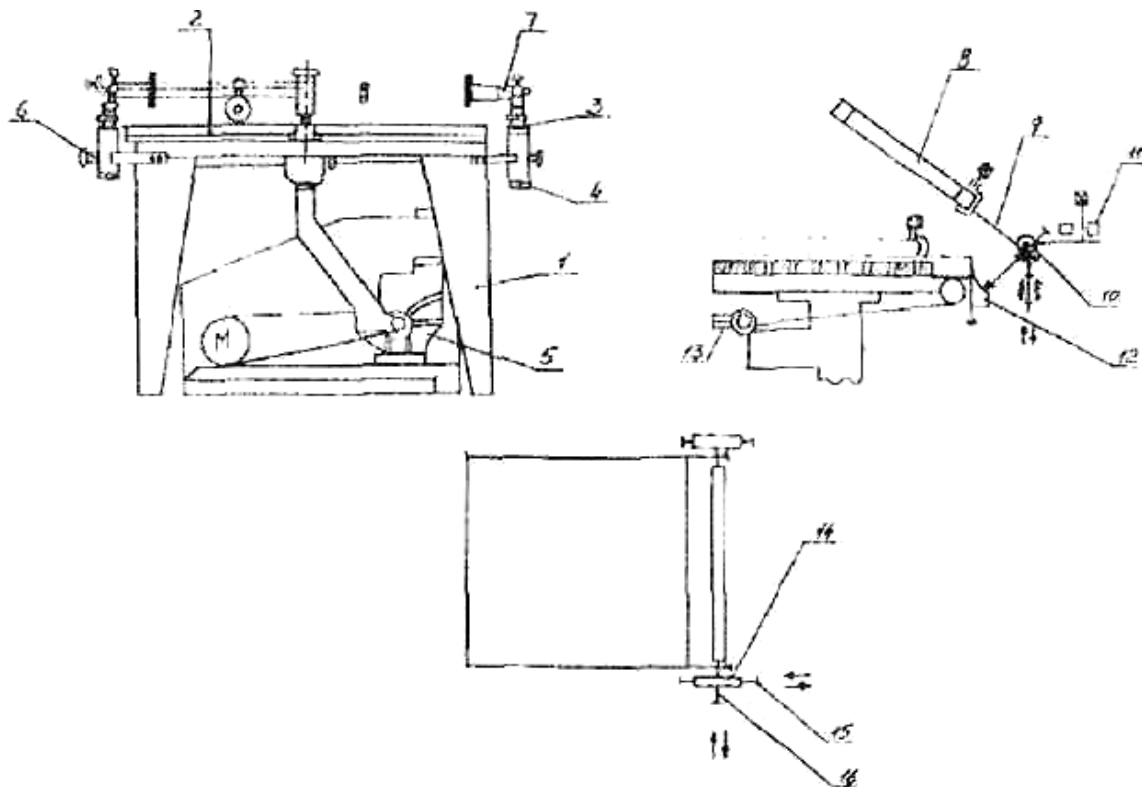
Схема верстату трафаретного друку ПТ-450 (1- каркас; 2 - друкарський стіл; 3, 4, 6- регулювання висоти форми; 5 -центробіжний вентилятор; 7, 14 - фіксуючі гвинти; 8 - форма; 9 -формоутримувач; 10 - вал; 11- противаги форми; 12 - упор; 13 - зсув; 15, 16 - регулюючі гвинти для здійснення приводки).
